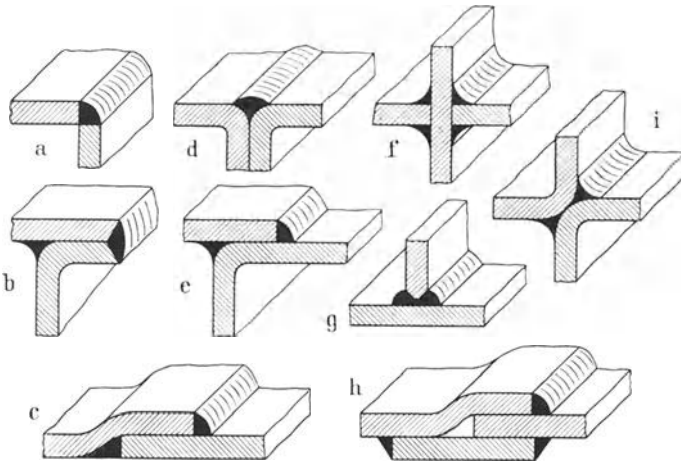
Ecken-, Kanten- und gekröpfte Schweißungen.
